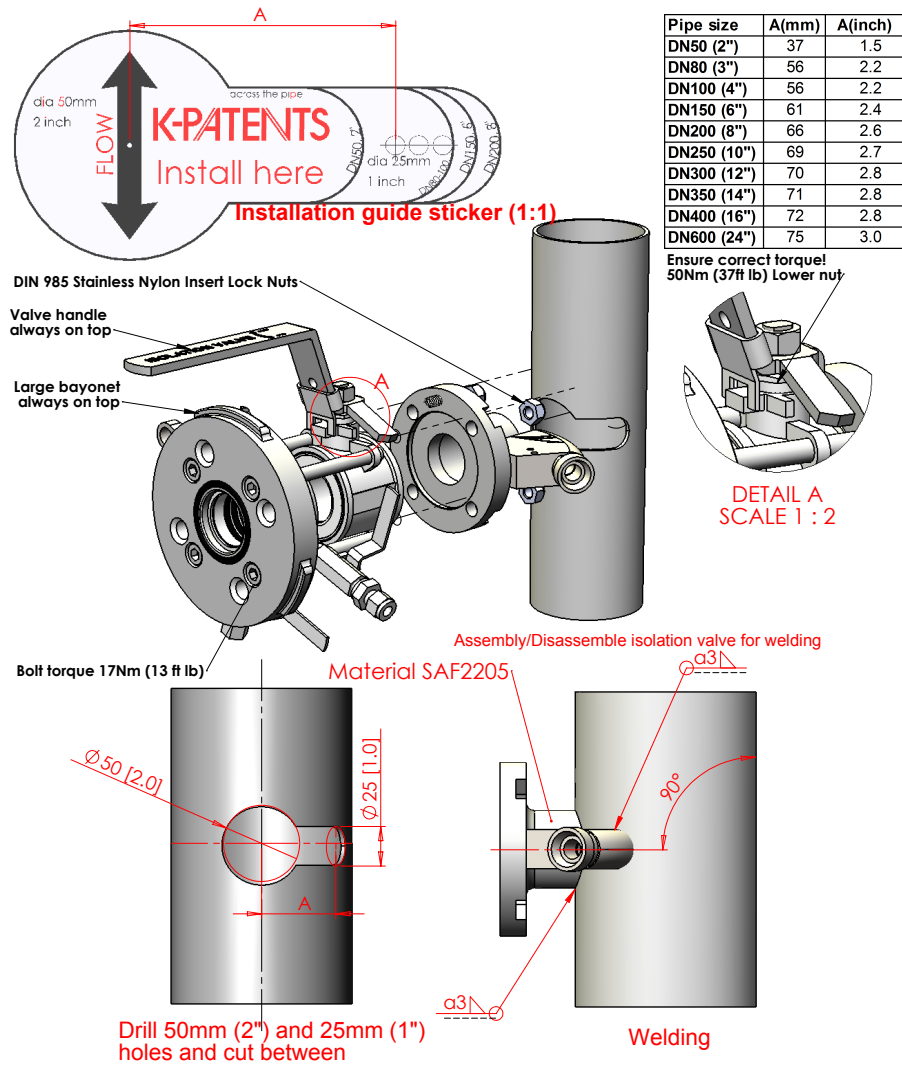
Soudage de la vanne d'isolement Safe-Drive™ à un tube vertical
